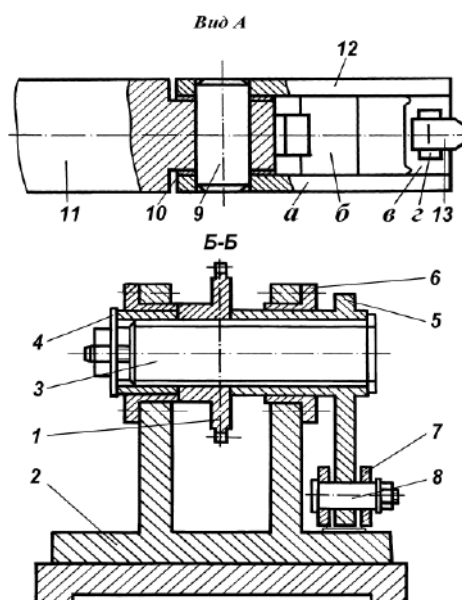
Вид на нагружающую скобу (Вид А) и разрез устройства для установки и фиксации зубчатого колеса на стенде (Б-Б)
